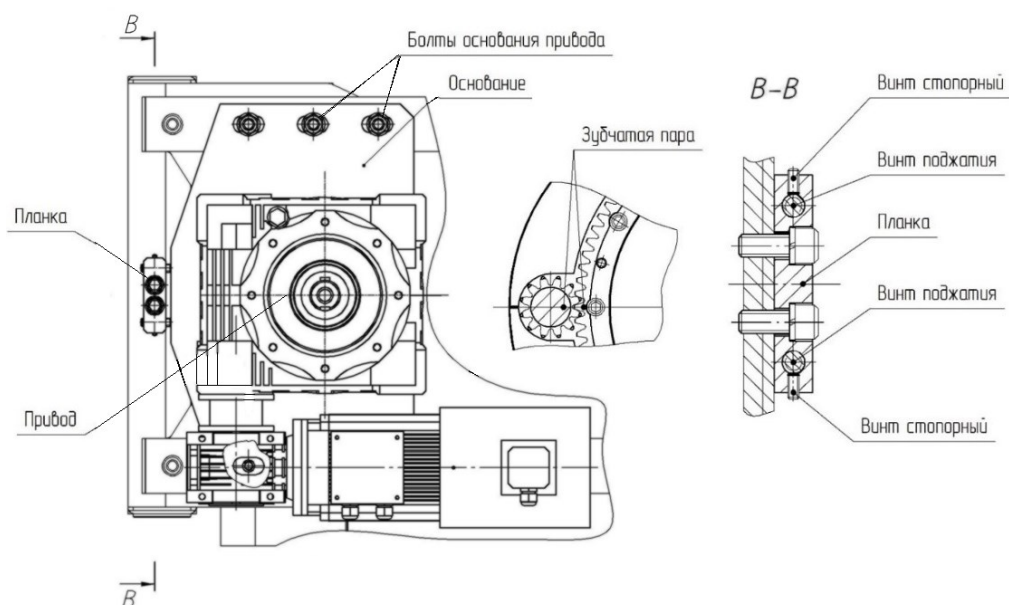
Выборка люфта зубчатой передачи по угломестной оси ОПУ
